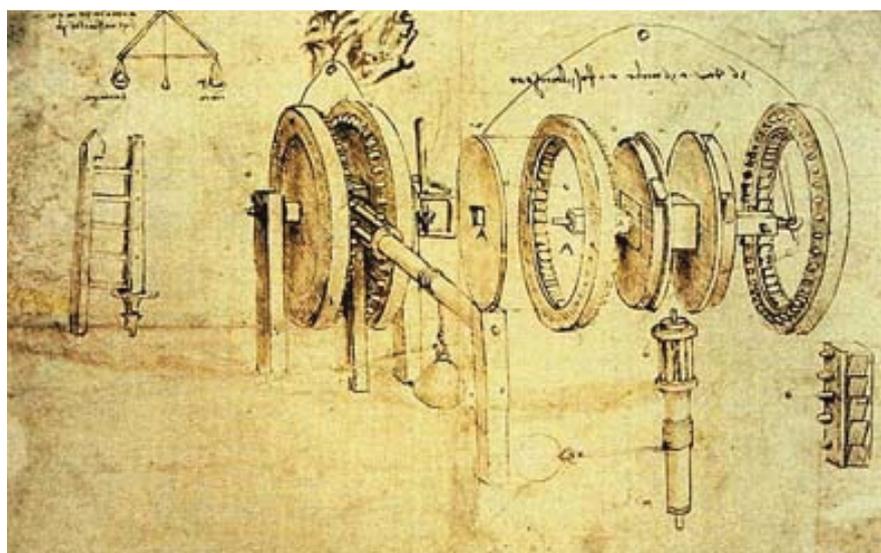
Frühe Explosionszeichnung von Leonardo da Vinci (1503)
